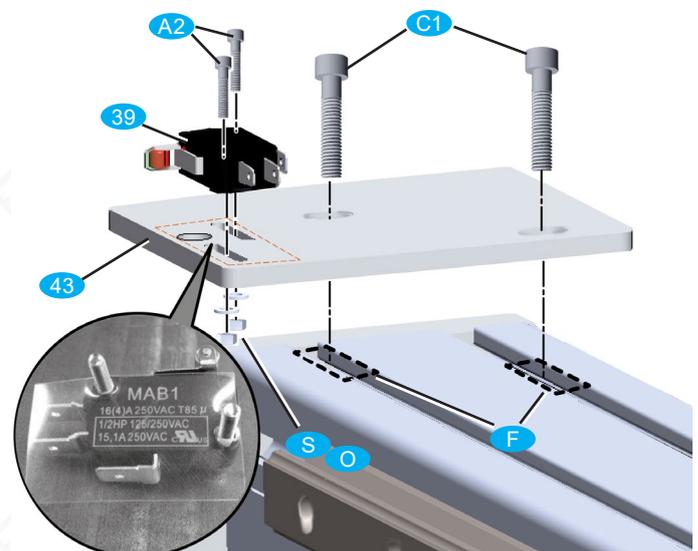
Referenzschalter Y. Schrauben C1 3 mm gekürzt.
